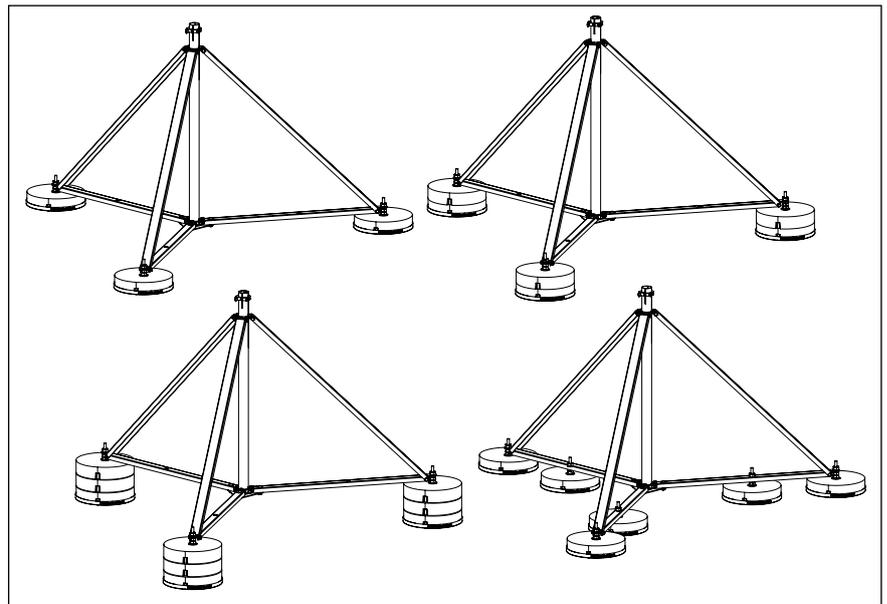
Erhöhung des Standgewichts durch Stapeln der Betonsteine
